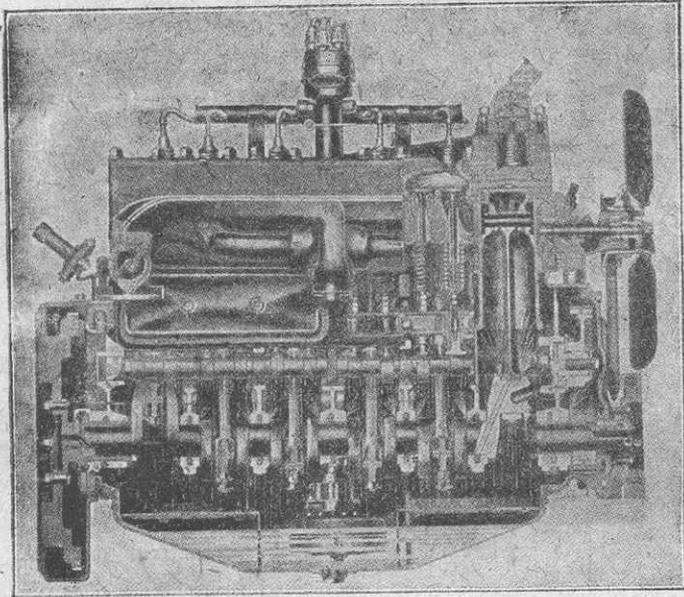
Продольный разрез шестицилиндрового двигателя «Крайслер», 12/55 л. с.
